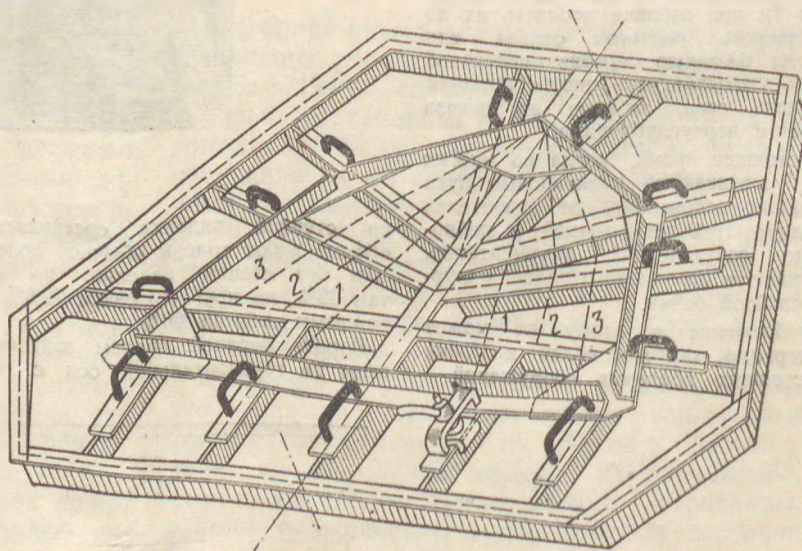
Кондуктор для сборки шпангоутных рам упрощенных обводов: 1 — рама сварного таврового профиля; 2 — шпангоутная рама; 3 — подложные зажимы
